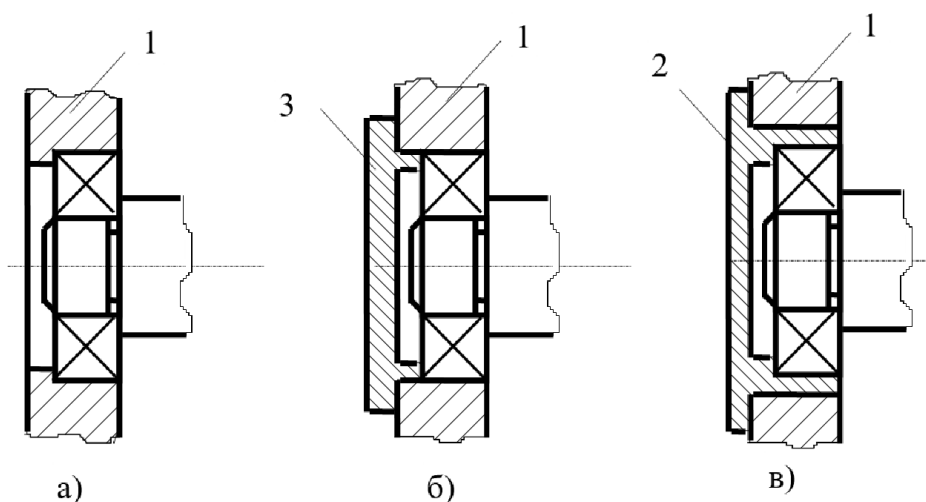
Схемы крепления подшипников в корпусе
